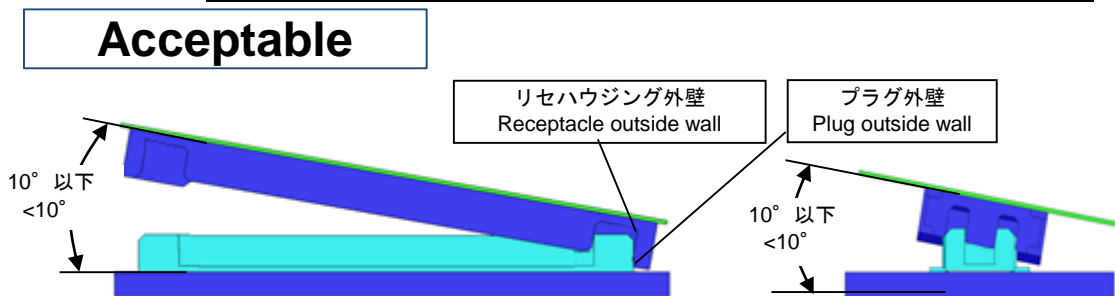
外壁合わせによる嵌合 Fig.2 Diagonal mating by aligning Plug outside wall
